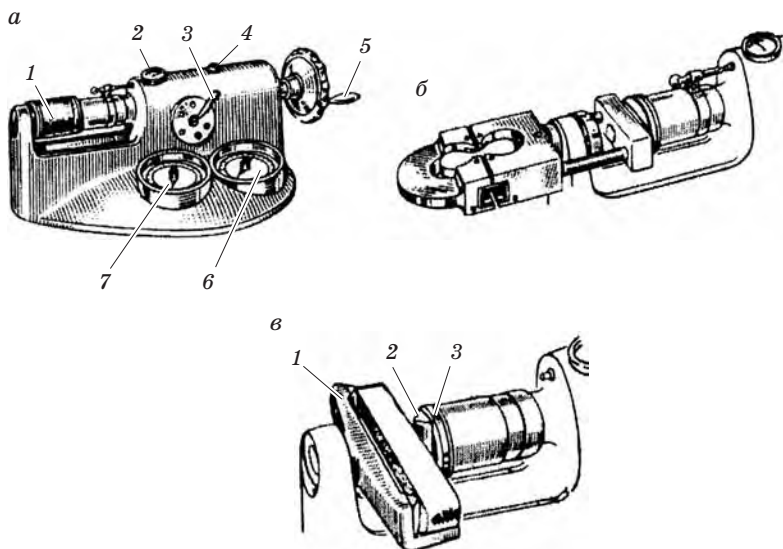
Универсальный прибор для определения прочности смесей на сжатие (а); дополнительное приспособление для испытания на разрыв (б); дополнительное приспособление для испытания на изгиб (в)
